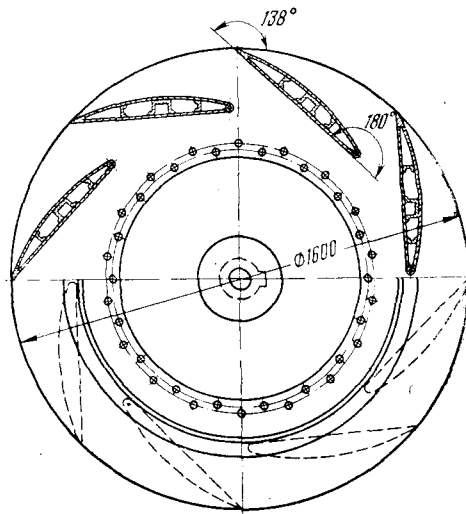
Рабочее колесо центробежного вентилятора нового типажа
